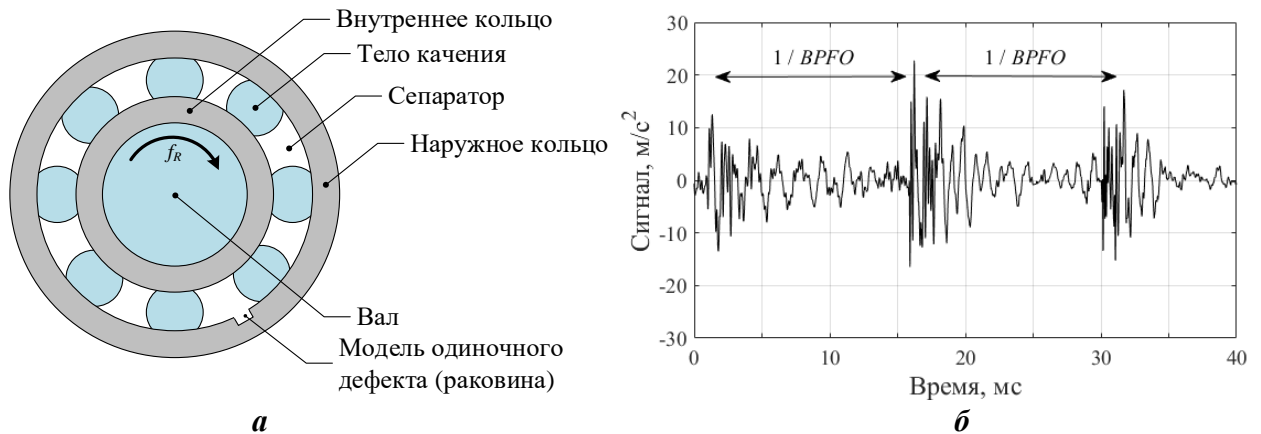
Анализ вибрации подшипника качения с раковиной на наружном кольце: *а* – схематичное изображение конструкции дефектного подшипника качения; *б* – фрагмент сигнала вибрации дефектного подшипника (последовательность экспоненциальных ударных импульсов)
